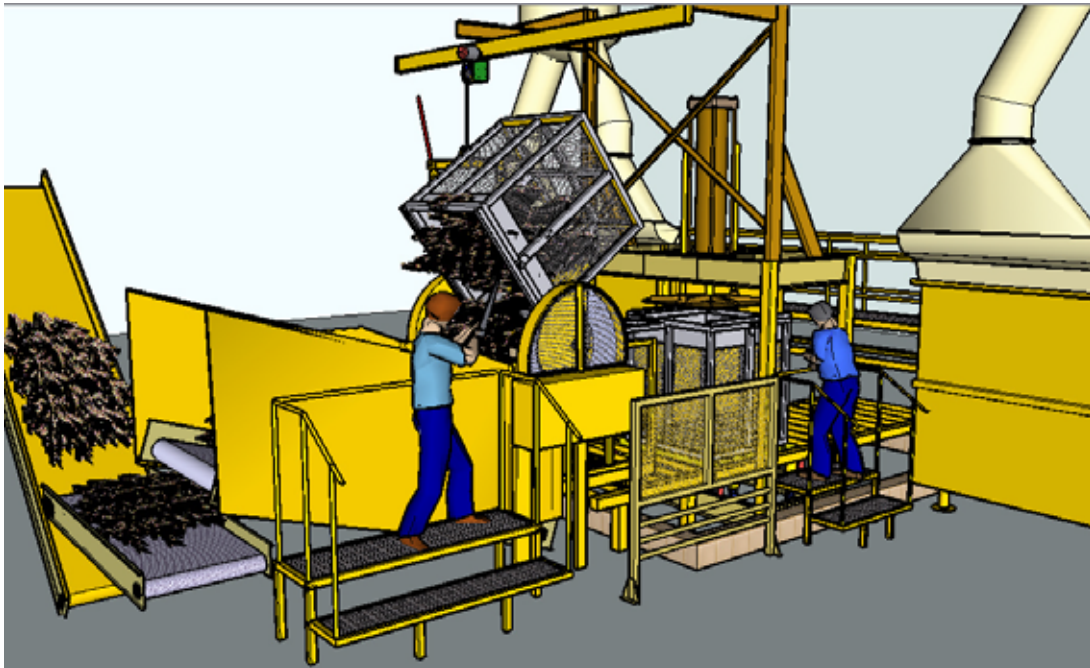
Imagen N° 1 del Dispositivo Propuesto
